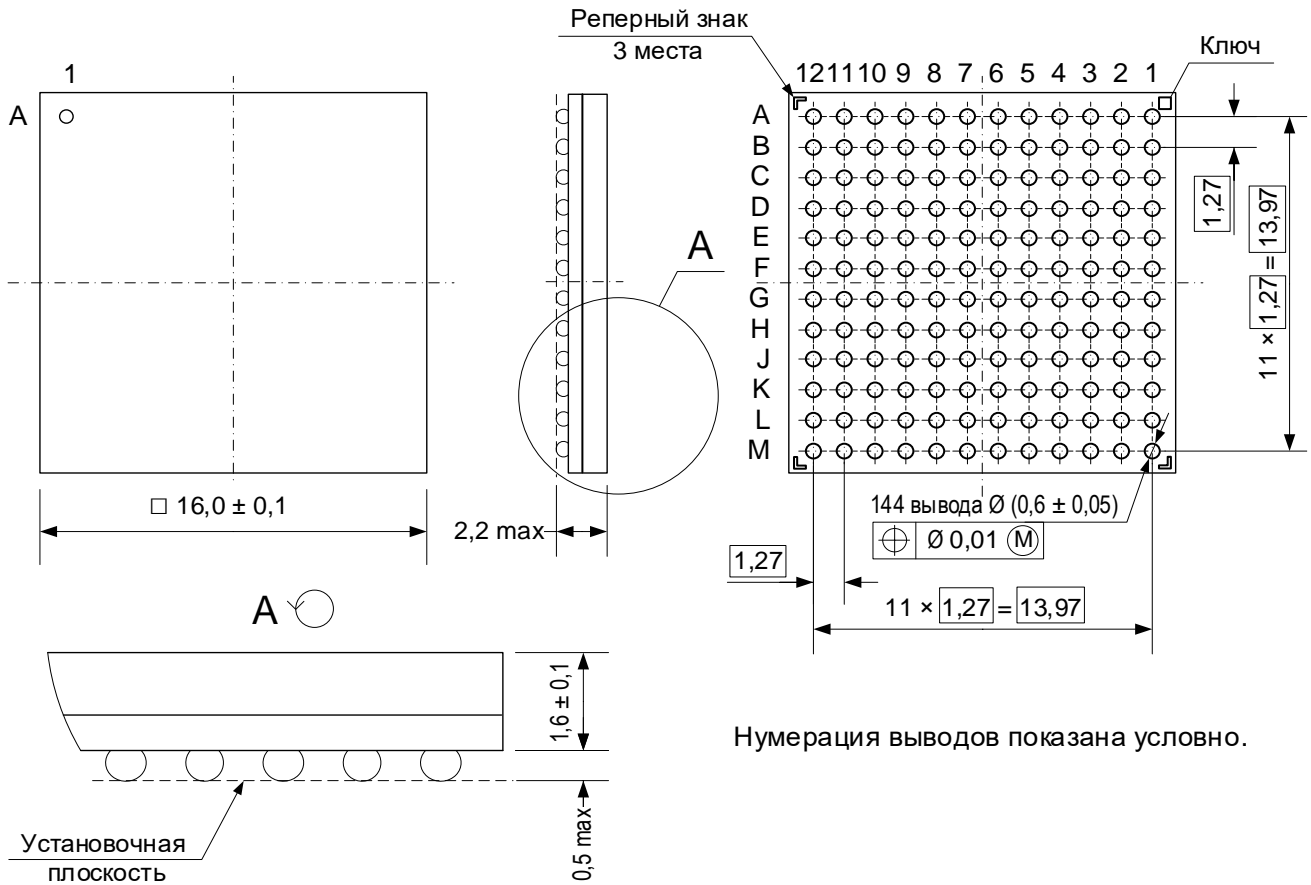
Габаритный чертеж микросхемы K1986BE1G1 в корпусе BGA144 16×16×1,6 (1,27)
